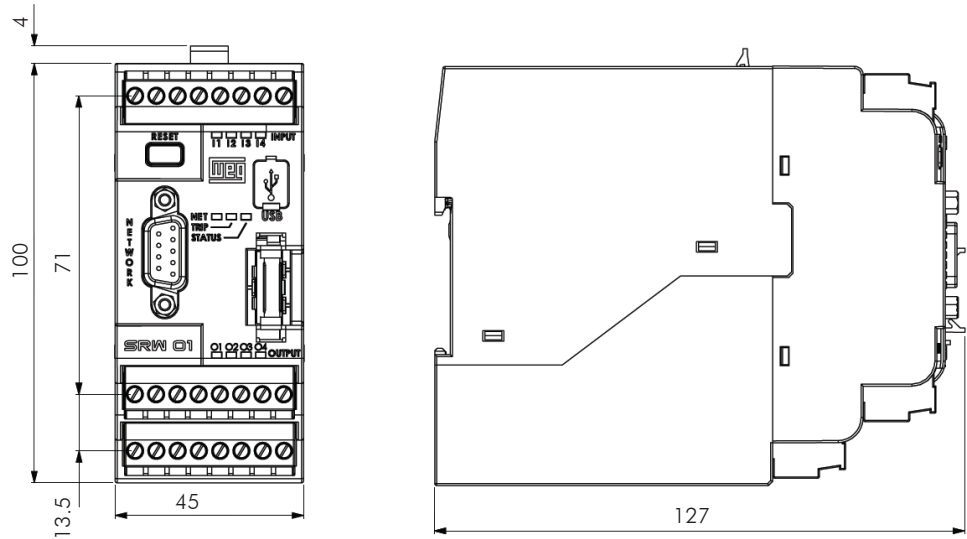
Dimensões da Unidade de Controle – UC (mm)
